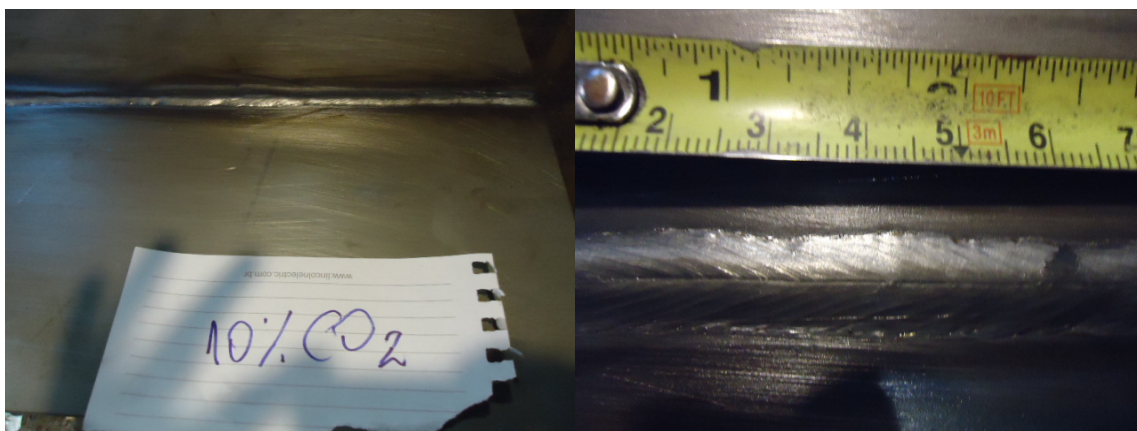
Chapa teste soldada com mistura 10% CO_2
